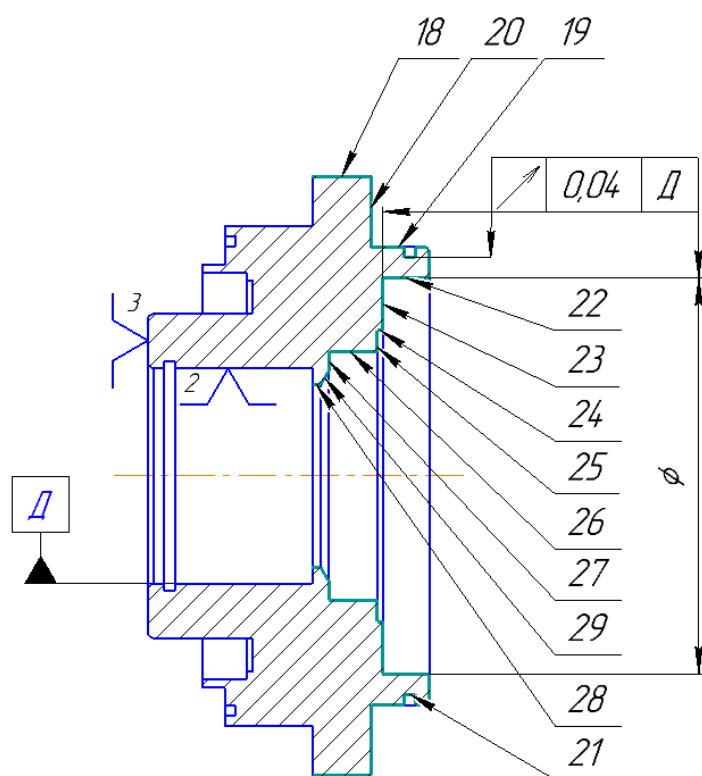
Эскиз токарной операции с ЧПУ, установ Б
